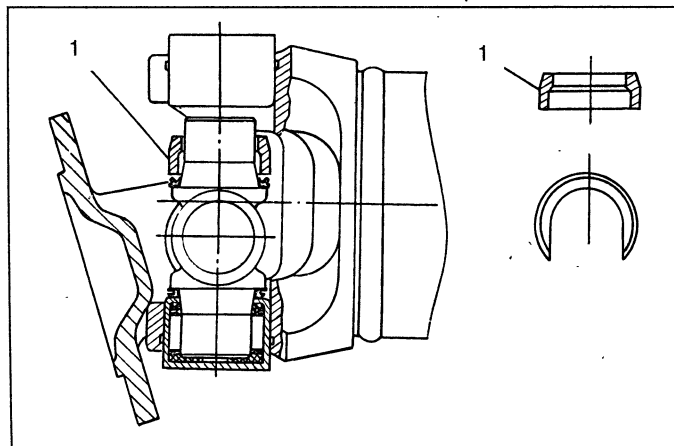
Установка втулки для разборки карданного шарнира: 1 – втулка
